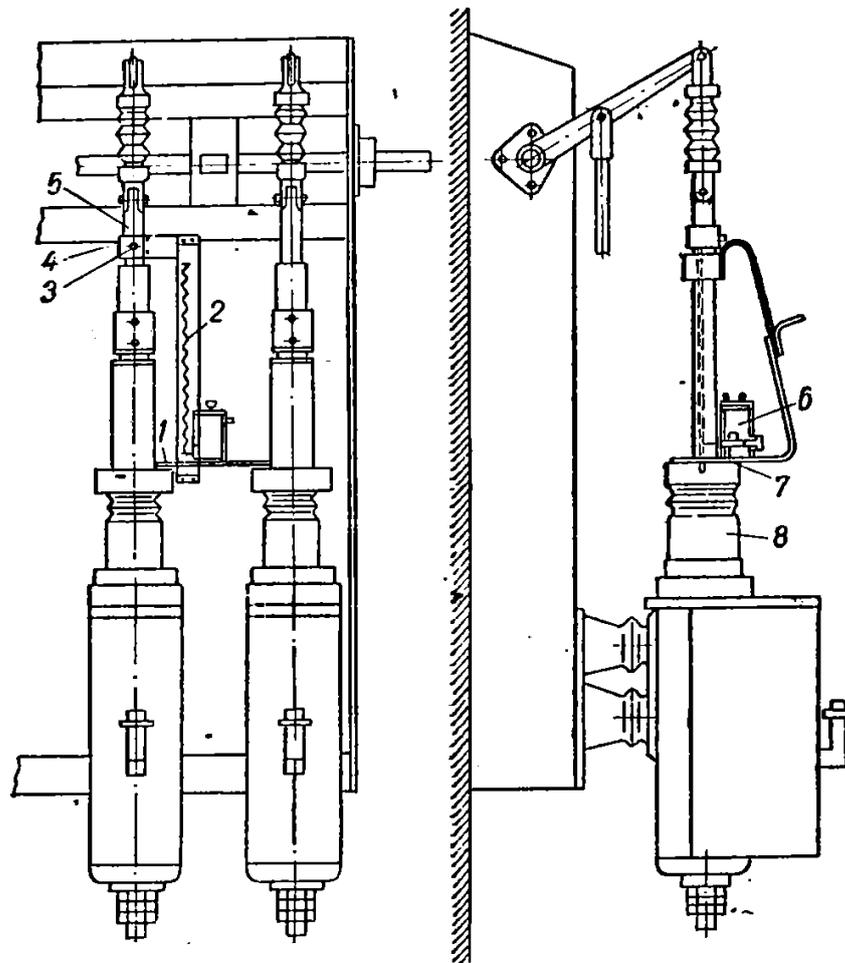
Установка вибрографа на выключателе ВМГ-133: 1- планка для установки вибрографа; 2 - планка с бумажной лентой; 3 - стопорный винт; 4 - хомут; 5 - изолятор - тяга; 6 - виброграф; 7 - болты для крепления планки к фланцам проходных изоляторов; 8 - проходные изоляторы.
